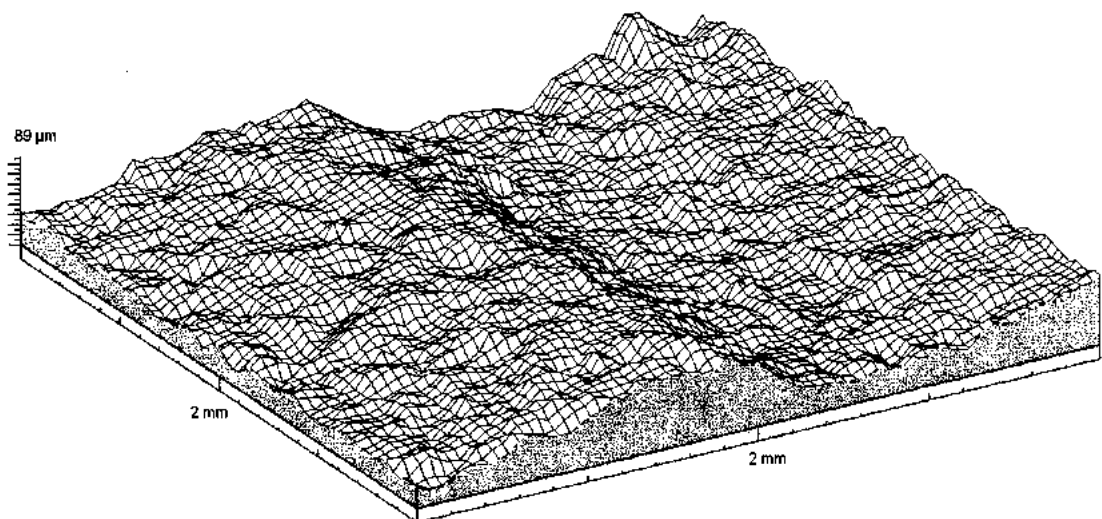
Аксонометричне зображення складної поверхні деталі після фрезерування
